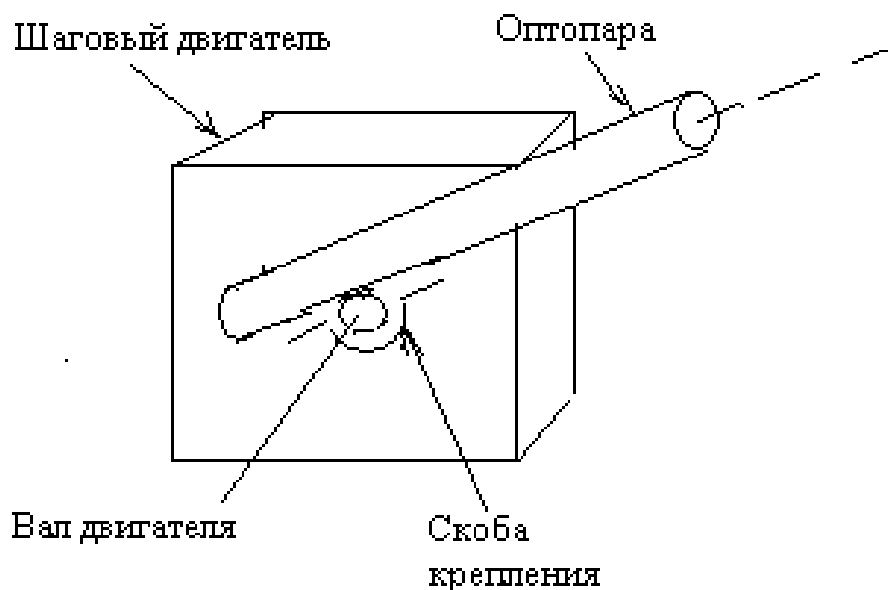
Схема конструктивная закрепления оптопары на валу шагового двигателя
